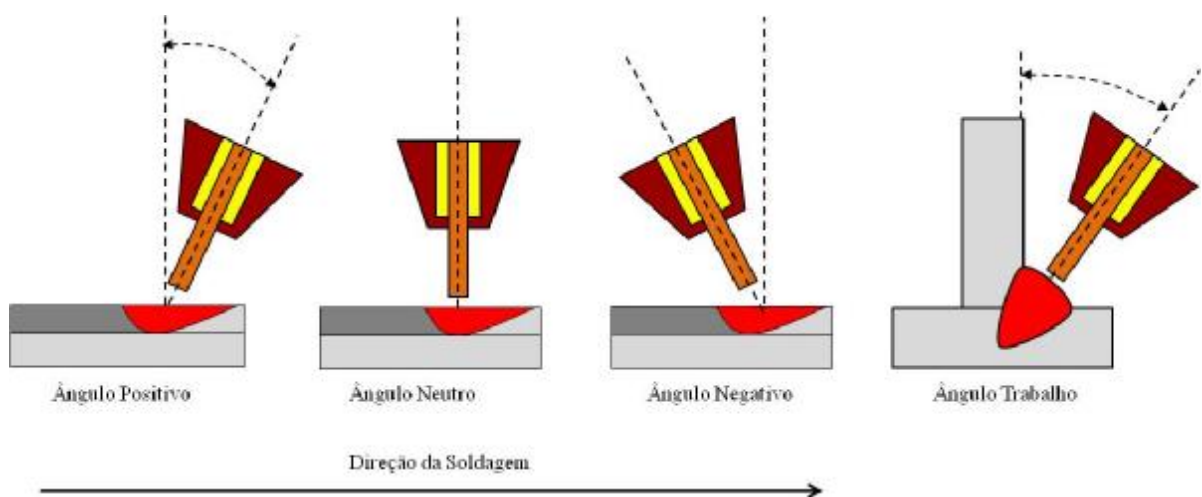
Efeito da posição do eletrodo e técnica de soldagem.
